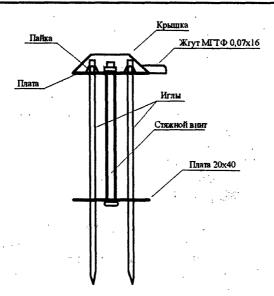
Конструкция щупа для прибора (М2:1)
